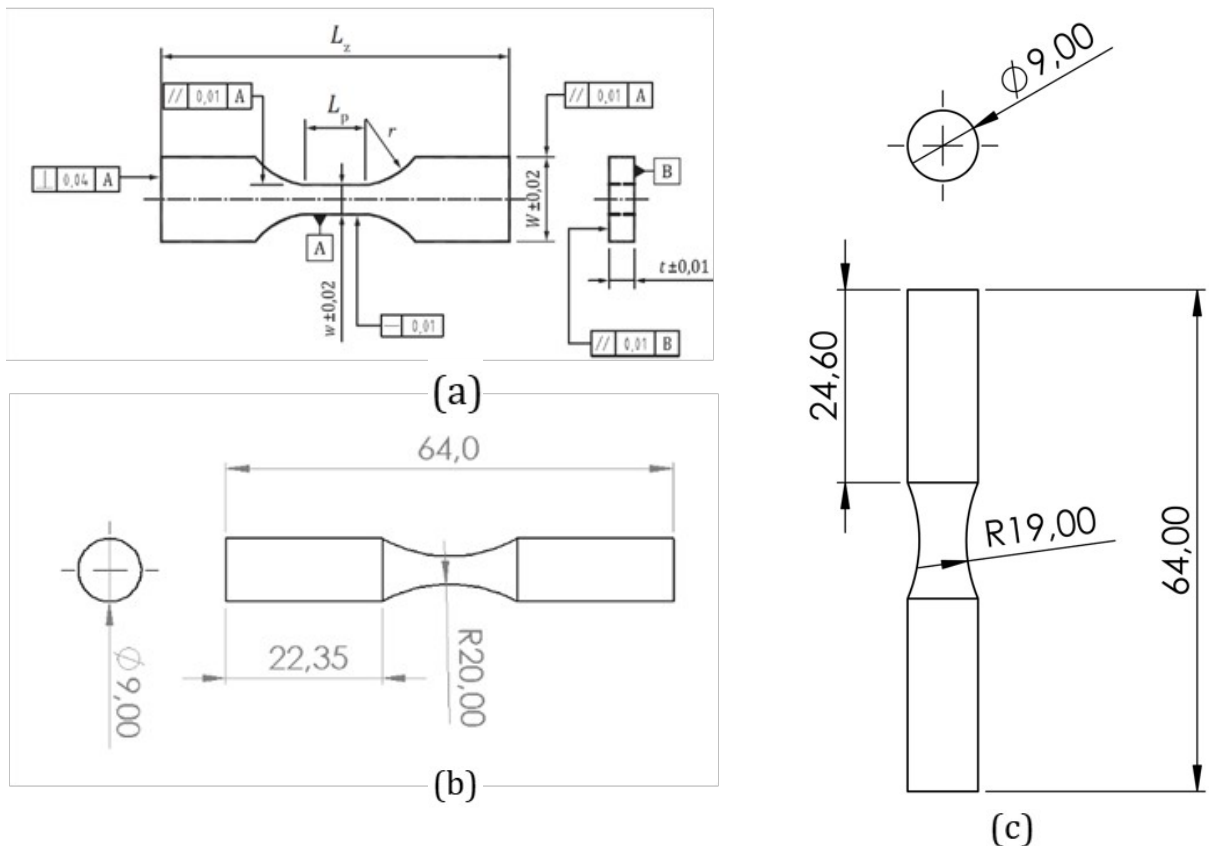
Cotas relacionadas a norma (a), geometria inicial dos corpos de prova (b) e geometria final dos corpos de prova impressos (c) (do autor) / Figure 4 - Dimensions related to the standard (a), initial specimen geometry (b), and final printed specimen geometry (c) (by the author)
